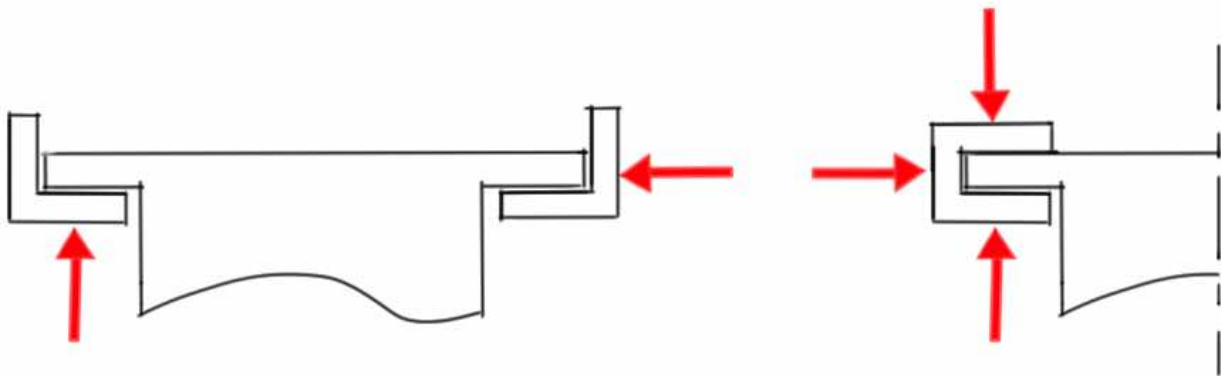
Plassering av festepunkt på aluminiumprofil i sitteflatestruktur.
